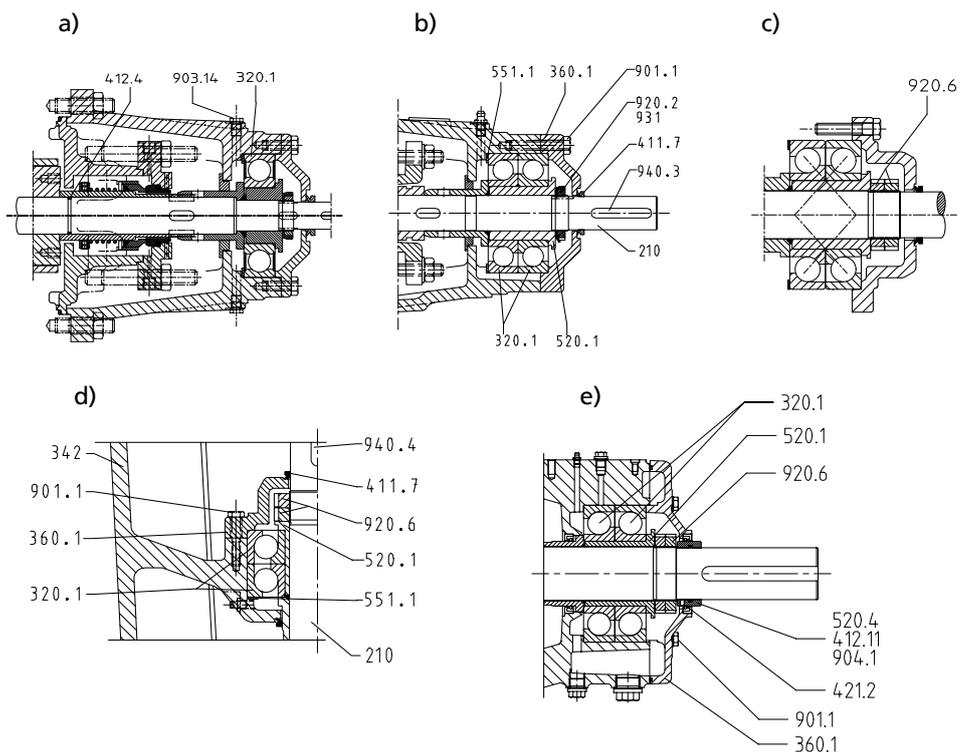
Консистентная смазка: а) типоразмер 32 и б) типоразмер 50-65 и с) типоразмер 100-200 и д) тип установки V при типоразмере 100-150 и е) типоразмер 250
